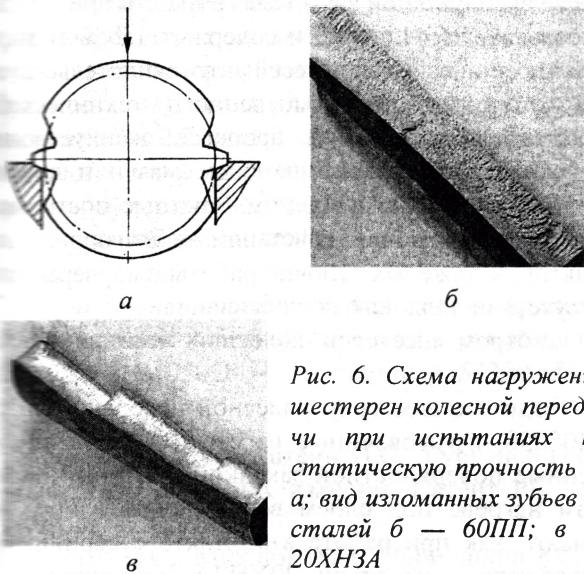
Схема нагружения шестерен колесной передачи при испытаниях на статическую прочность — а; вид изломанных зубьев из сталей б — 60ПП; в — 20ХНЗА
